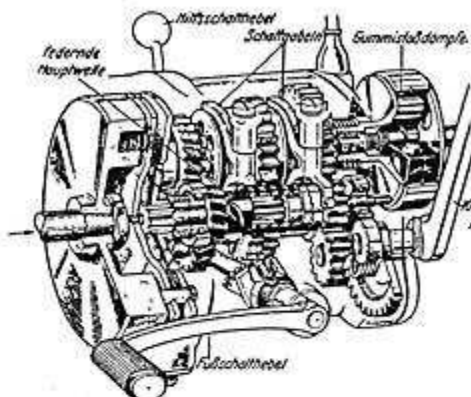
Vier-Gang-Wechselgetriebe des BMW-Kraffrades R 24, schen-Fußschaltung, Handschaltung, federnde Hauptwelle, Gummkupplung vor dem Kardantrieb
